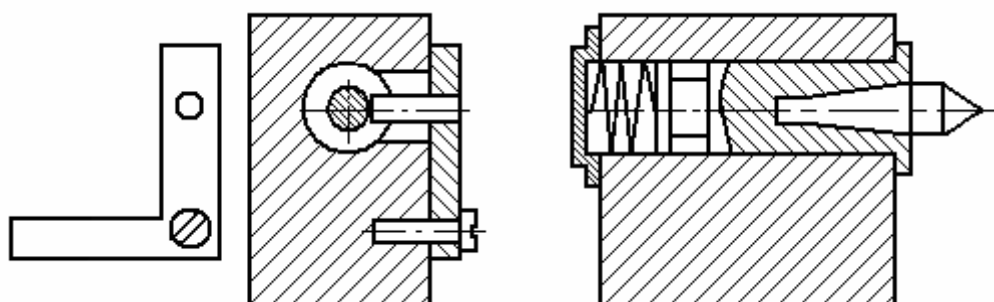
Расположение рычага сбоку от корпуса
